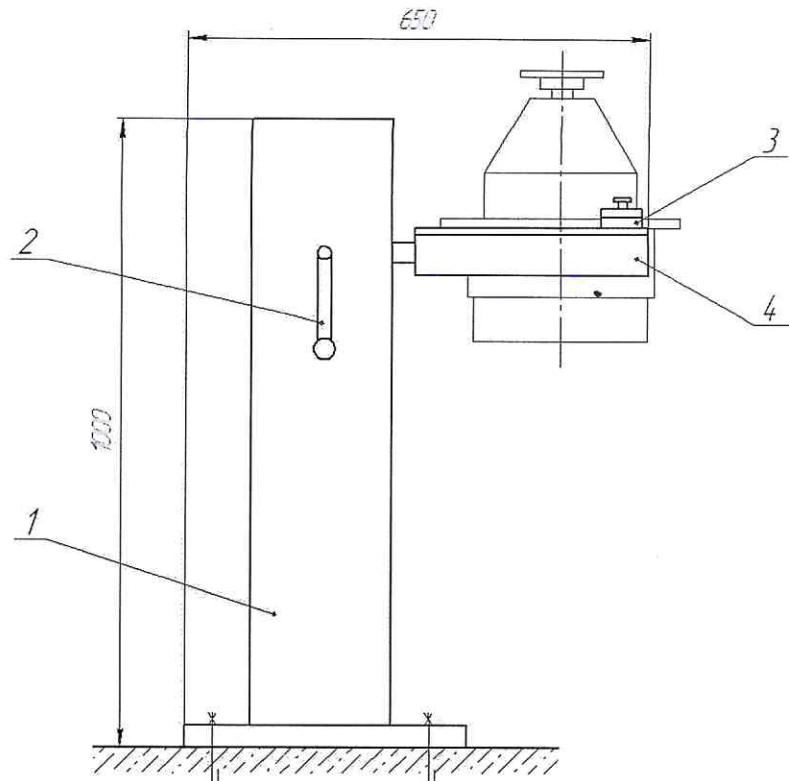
Стенд для разборки-сборки редуктора трансмиссии автомобиля КАМАЗ: 1-корпус; 2-рукоятка; 3-механизм зажима; 4-поворотная рама.
